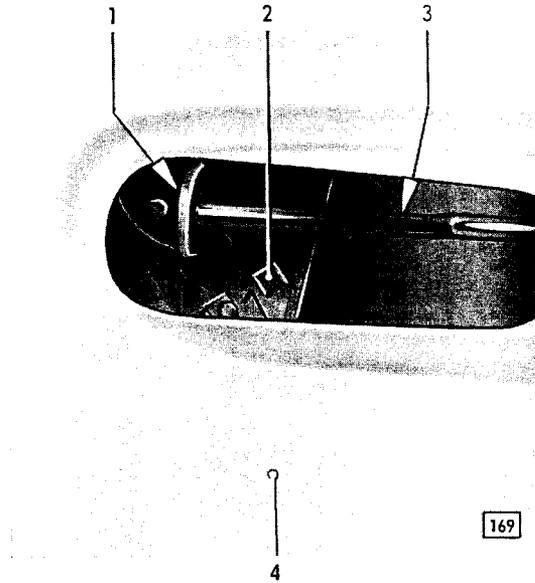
Zugstange für Fernbetätigung an Türschloß
